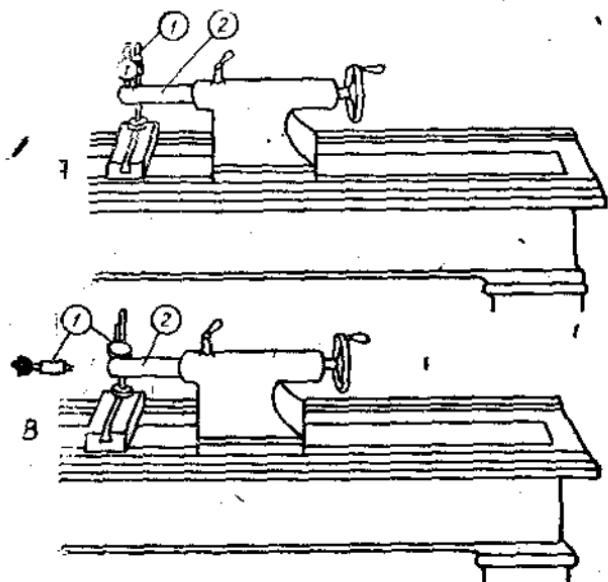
Проверка параллельности оси шпинтона задней бабки токарного станка направляющим станины.
